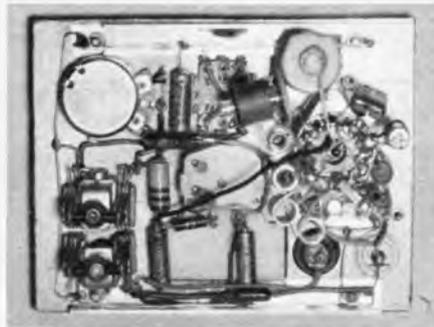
Rückansicht der Frontplatte mit der vollständigen Verdrahtung
